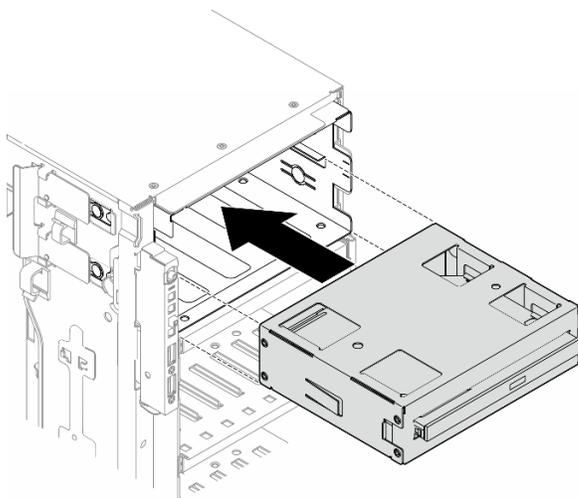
Installation einer Baugruppe für das optische Laufwerk
